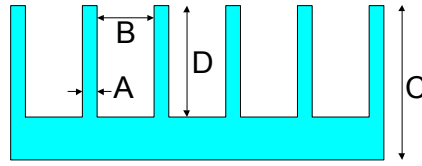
Vista esquemática de las columnas de vidrio. A) Anchura de las columnas, B) distancia entre dos columnas, C) espesor de la oblea de vidrio y D) altura de las columnas
